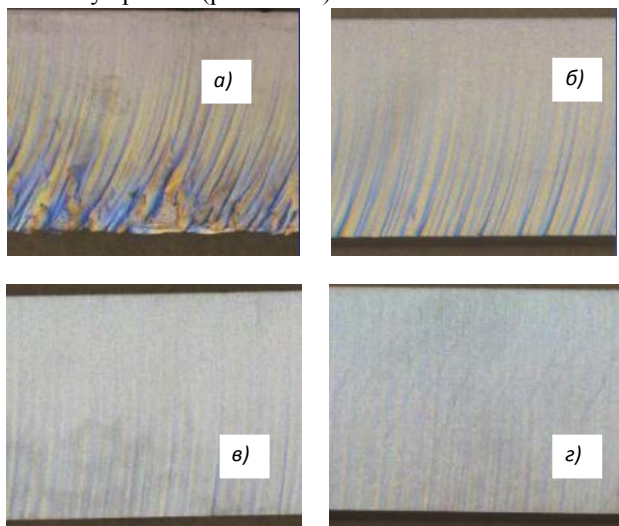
Неравномерность шероховатости кромки обрабатываемого материала значительной толщины (материал – Сталь 40Х, толщина – 25 мм); для повышения качества скорость контурной подачи снижена в 4 раза
